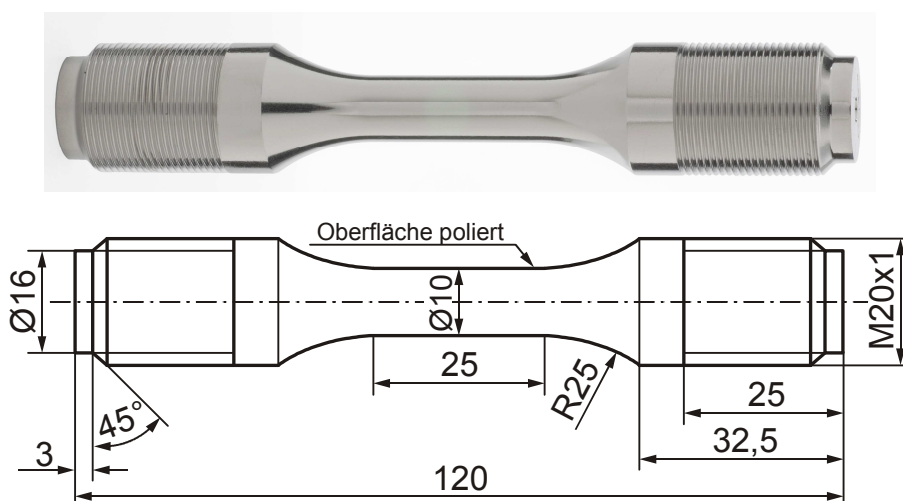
MPA-Schwingversuchsprobe: (oben) reale Probe; (unten) technische Zeichnung.
